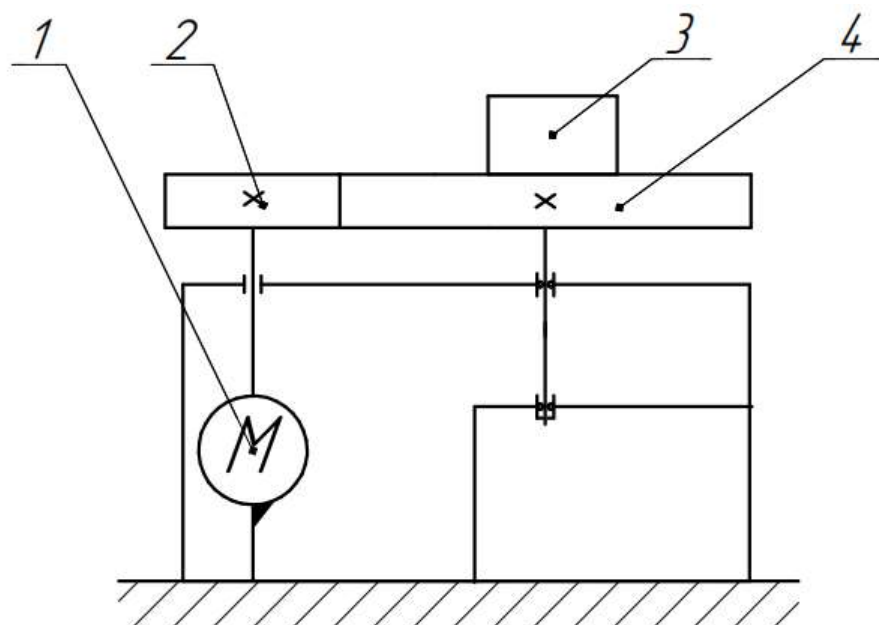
Кинематическая схема. 1- двигатель, 2- шестерня, 3- камера, 4- зубчатое колесо
